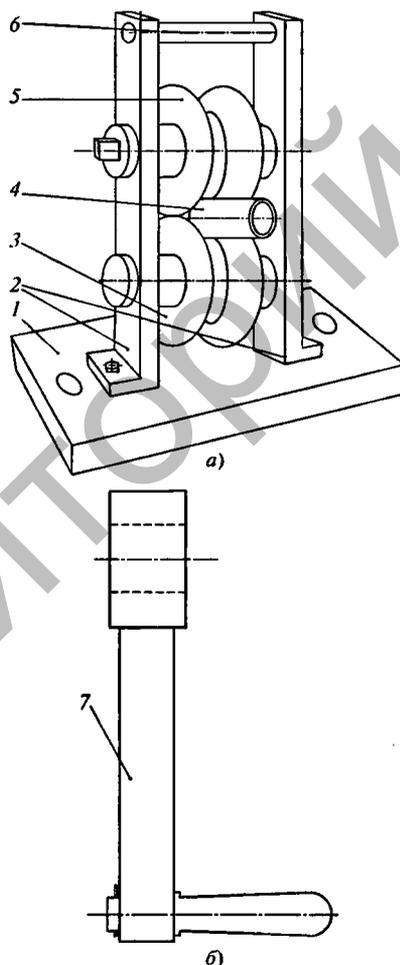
Общий вид установки с вращающимися матрицами (а) и ручки привода роликов (б):
